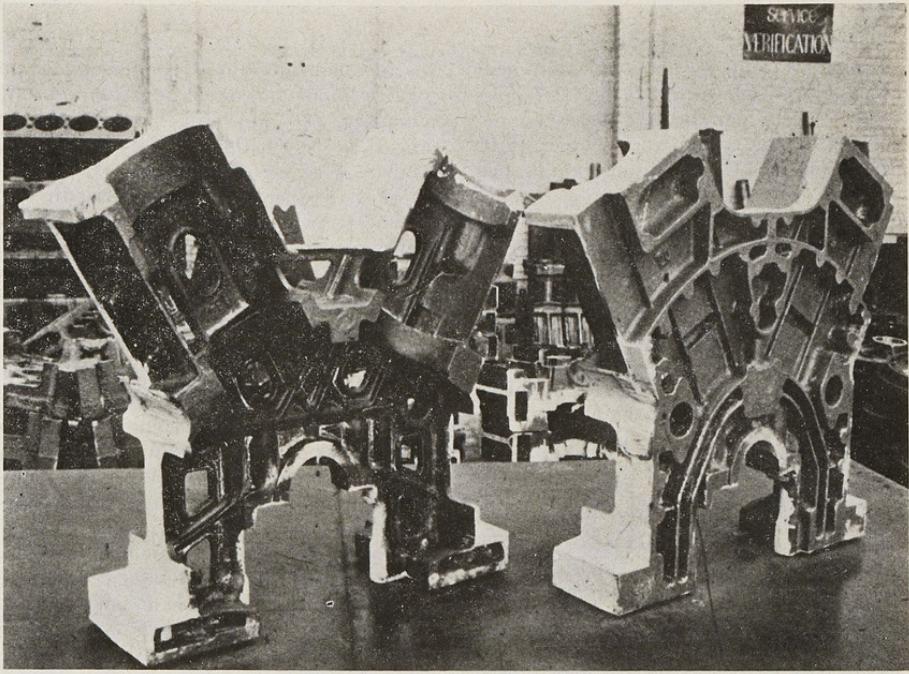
Exemple de réalisation d'un bâti de moteur par éléments moulés, réunis par soudage : photographies extraites du « guide de tracé des pièces en acier moulé ».
